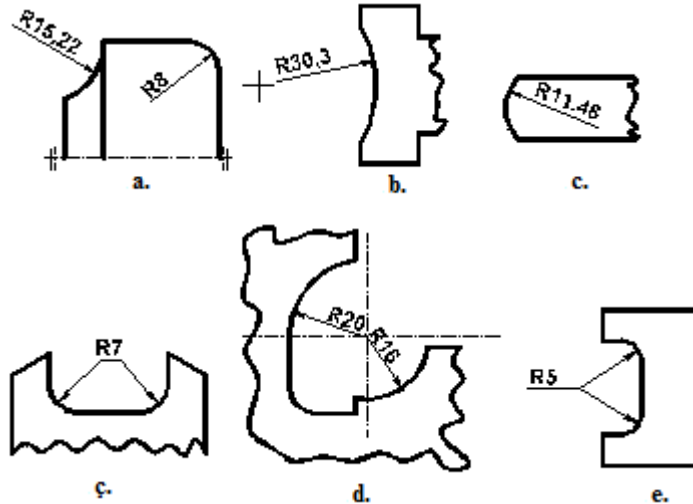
Şekiller üzerinde çapların ölçülendirilmesi
